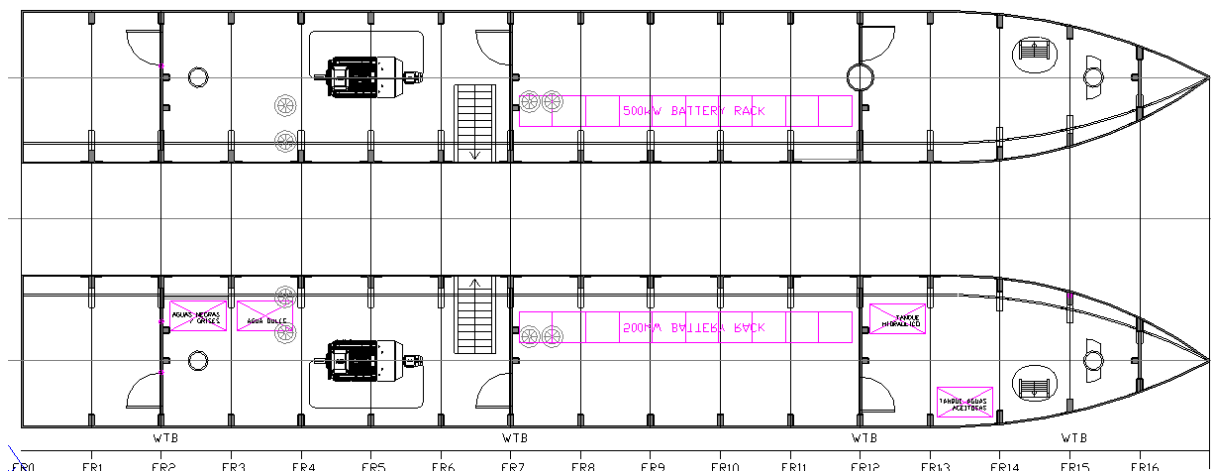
Vista en planta de las cuadernas y mamparos estancos bajo cubierta. Elaboración propia.
